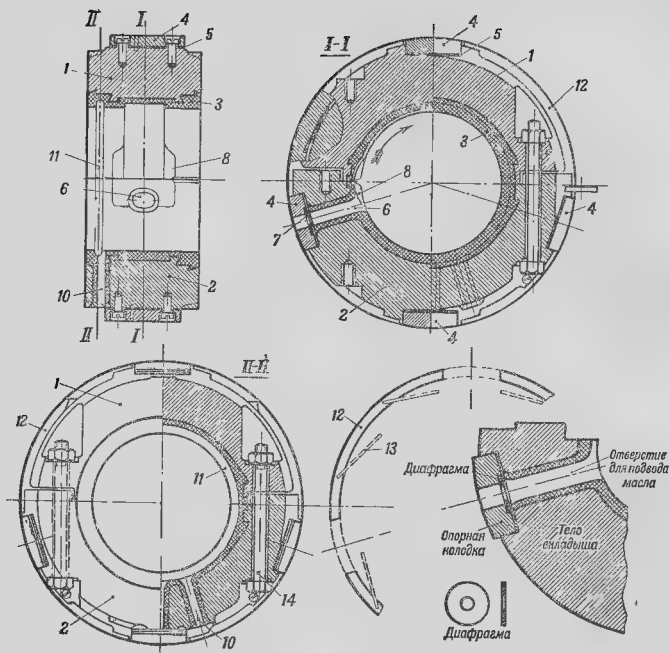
Вкладыш опорного подшипника турбины ЛМЗ
